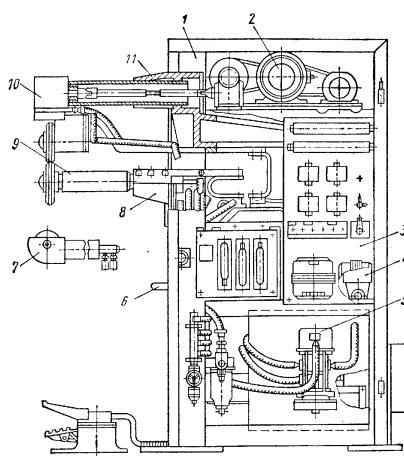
Машина типа МШ-1001 для шовной сварки: 1 — корпус машины; 2 — привод вращения типа ПМСМ; 3 — электрическое устройство; 4 — пневматический привод сжатия; 5 — пневматическое устройство; 6 — винтовой домкрат для подъема нижнего кронштейна; 7 — электродное устройство для продольной сварки; 8 — нижний кронштейн; 9 — нижнее электродное устройство для поперечной сварки; 10 — верхнее электродное устройство; 11 — верхний рычаг
